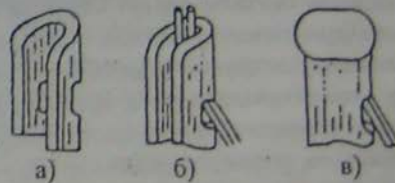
Получение контактного соединения при электромонтаже сваркой
